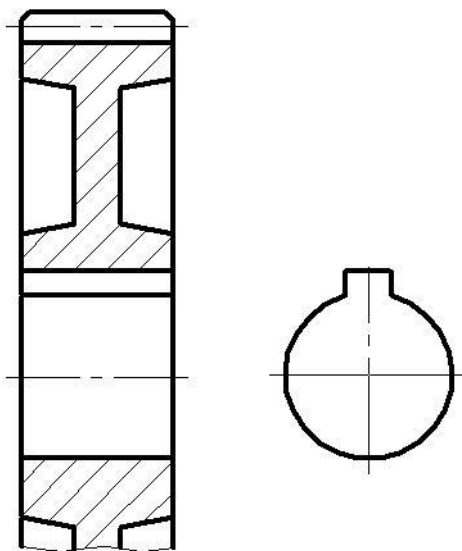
Вигляд на отвір зубчастого колеса
